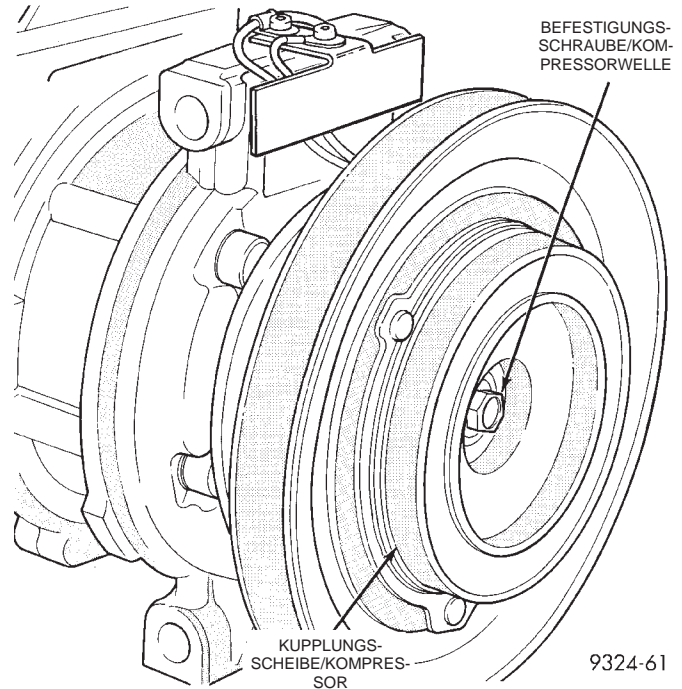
Befestigungsschraube der Kompressorwelle und Kupplungsscheibe
